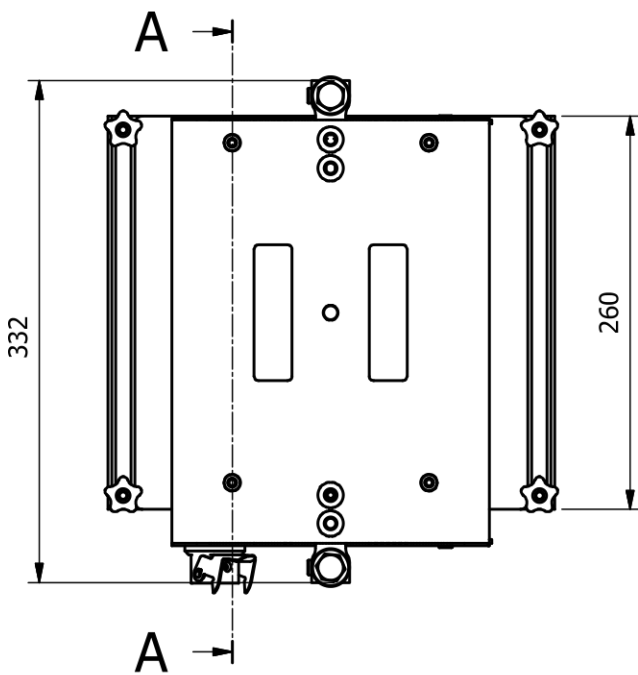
H08D016622 Schweißplatte PML-100
